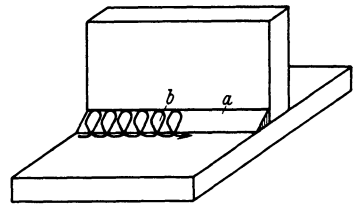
Elektrodenführung bei Kehlschweißung.
